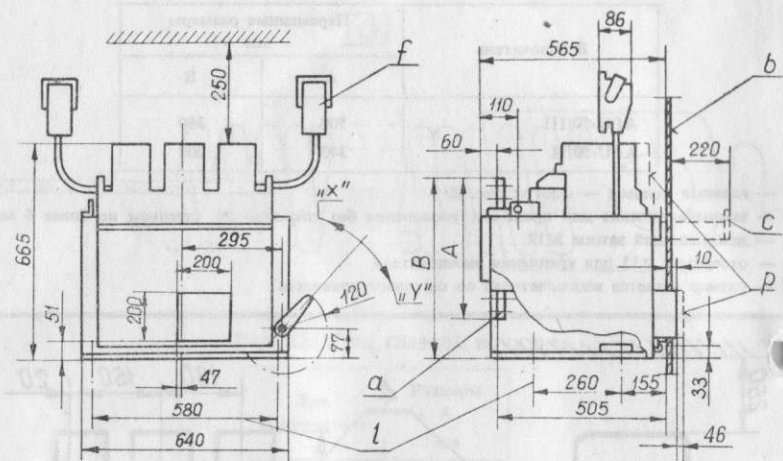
Размеры выключателей типа АРУ-50А с электродвигательным приводом, или же приспособленных для крепления ручного щитового привода
